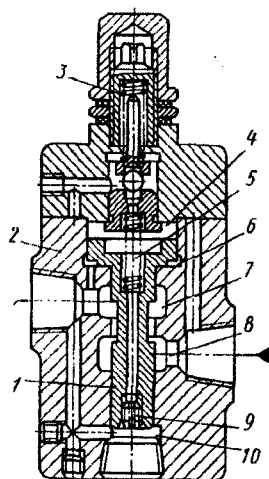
Редукционный клапан: 1 – золотник, 2 – корпус, 3, 5 – пружина, 4, 6, 7, 8, 10 – полость, 9 – пробка
